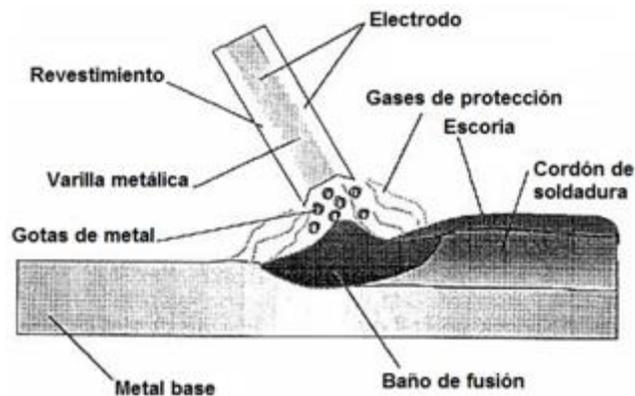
Soldadura con electrodo revestido. [4]
